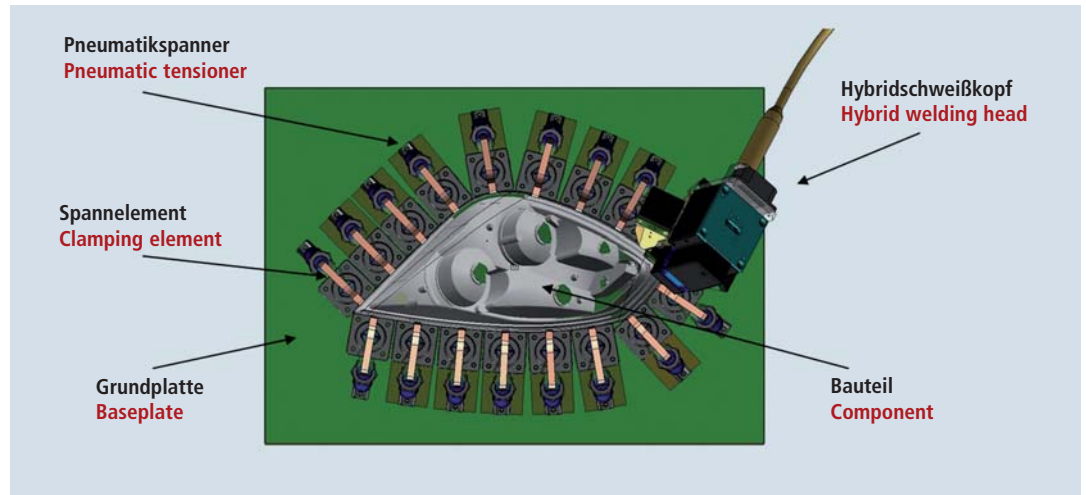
Bearbeitungskopf mit Spanntechnik fürs Hybridschweißen in der Aufsicht
